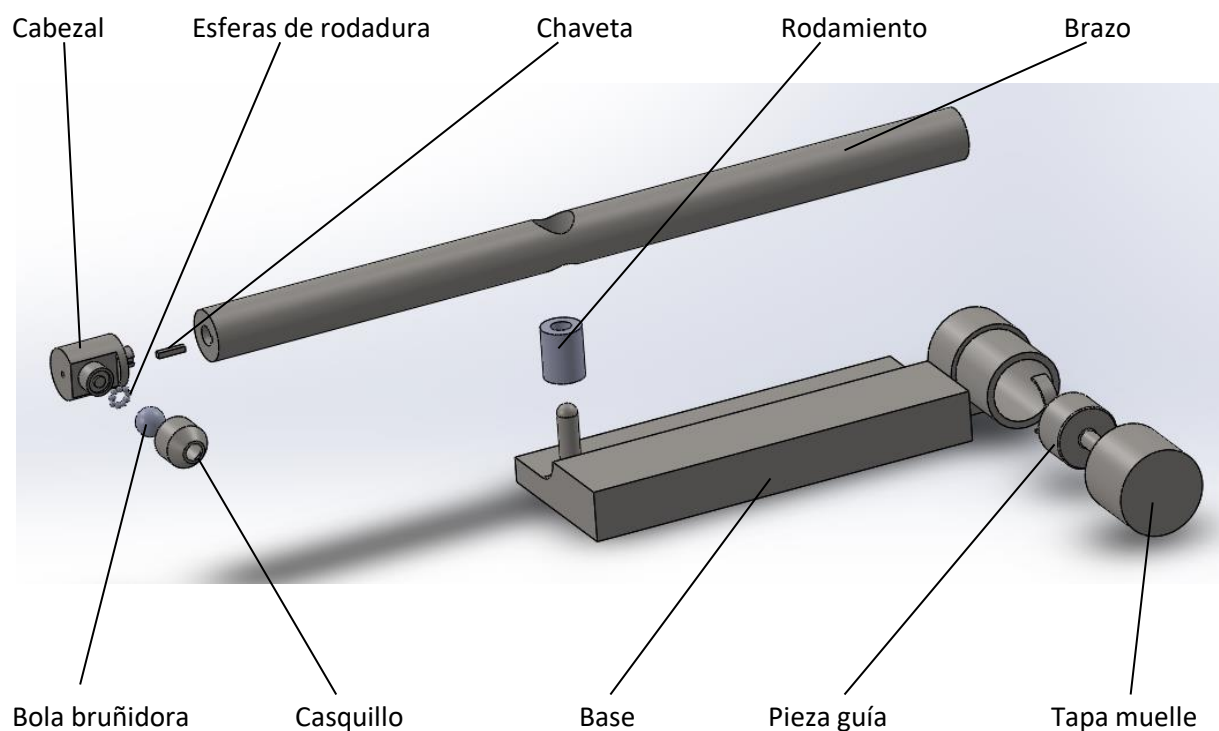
Vista explosionada de la herramienta de bruñido con bola.
